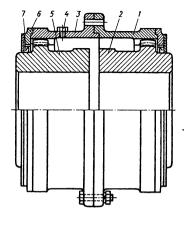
Муфта зубчатая: 1 и 3 — обоймы; 2 и 5 — втулки; 4 — пробка; 6 — крышка; 7 — резиновое уплотнение манжетного типа
